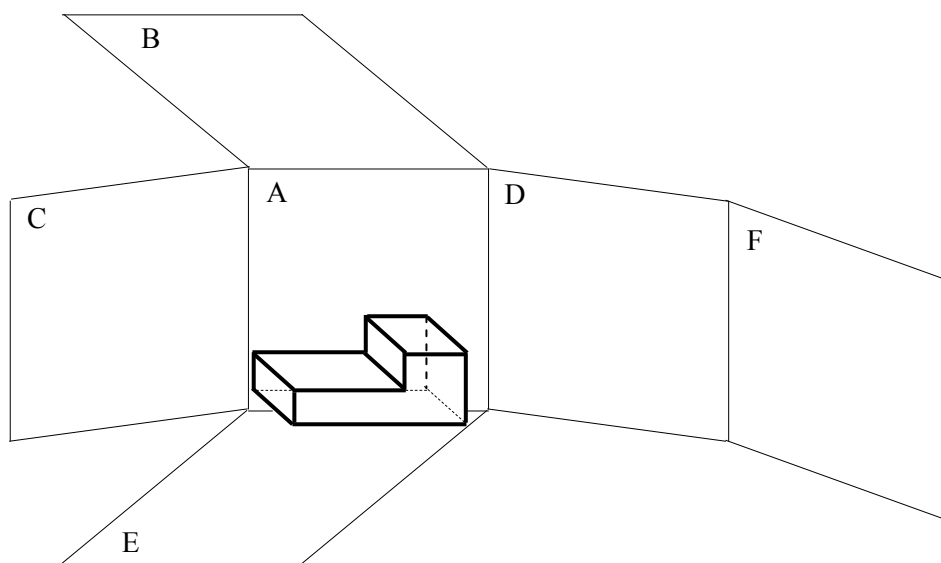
Desfășurarea cubului de proiecție în plan, conform metodei de proiecție americane
